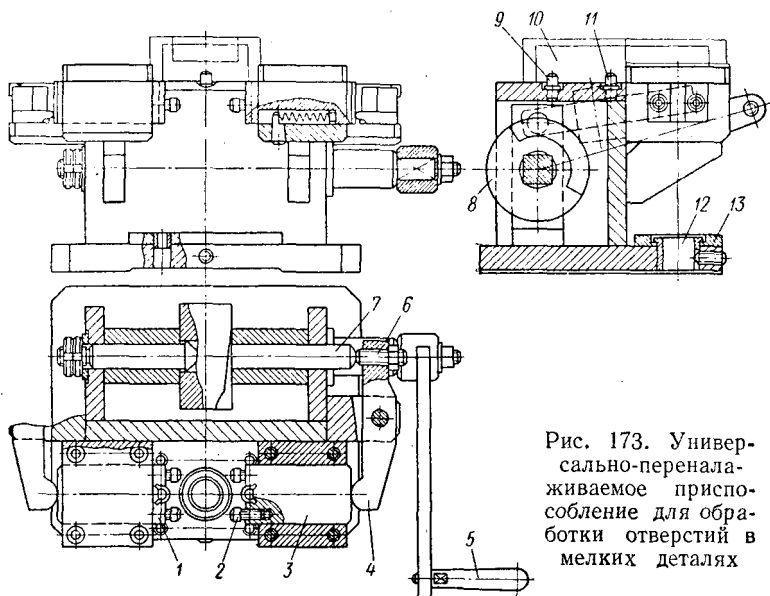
Универсально-переналаживаемое приспособление для обработки отверстий в мелких деталях
